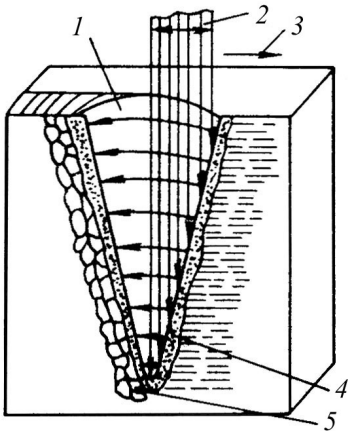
Схема руху розплавленого металу при ЕПЗ:
